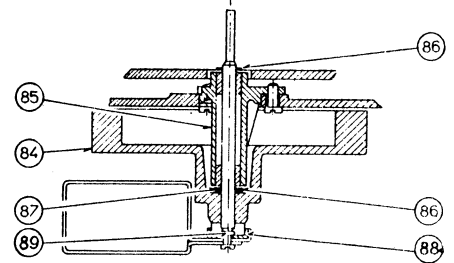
Náhradní součásti tlačítkové soupravy 30
